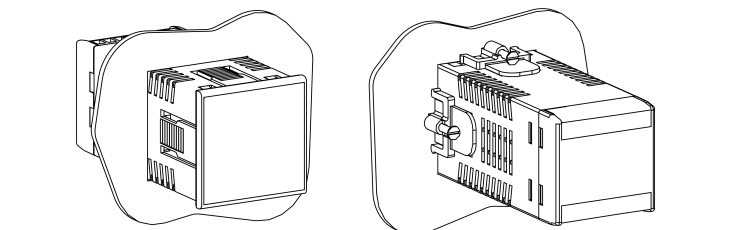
Монтаж прибора щитового крепления Щ5
